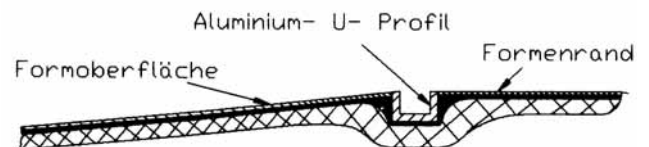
Das eingesetzte Aluminiumprofil an der Formkante ermöglicht ein definiertes und einfaches Besäumen der Bauteile.
